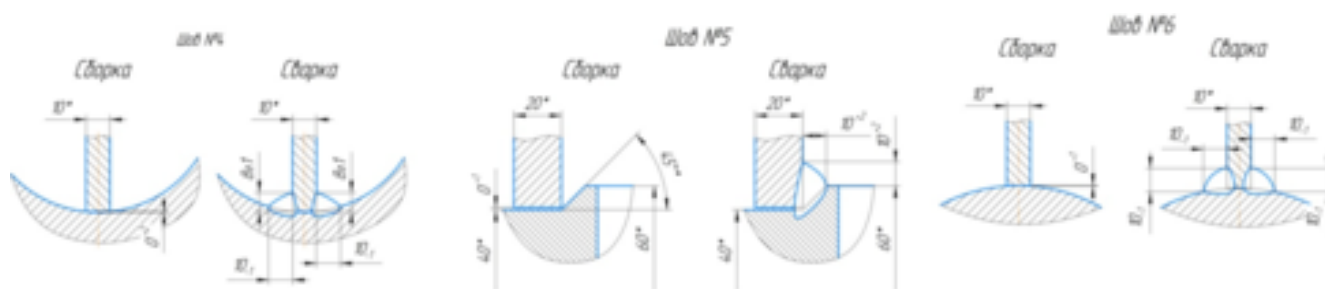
Сварные швы №4, №5 и №6
